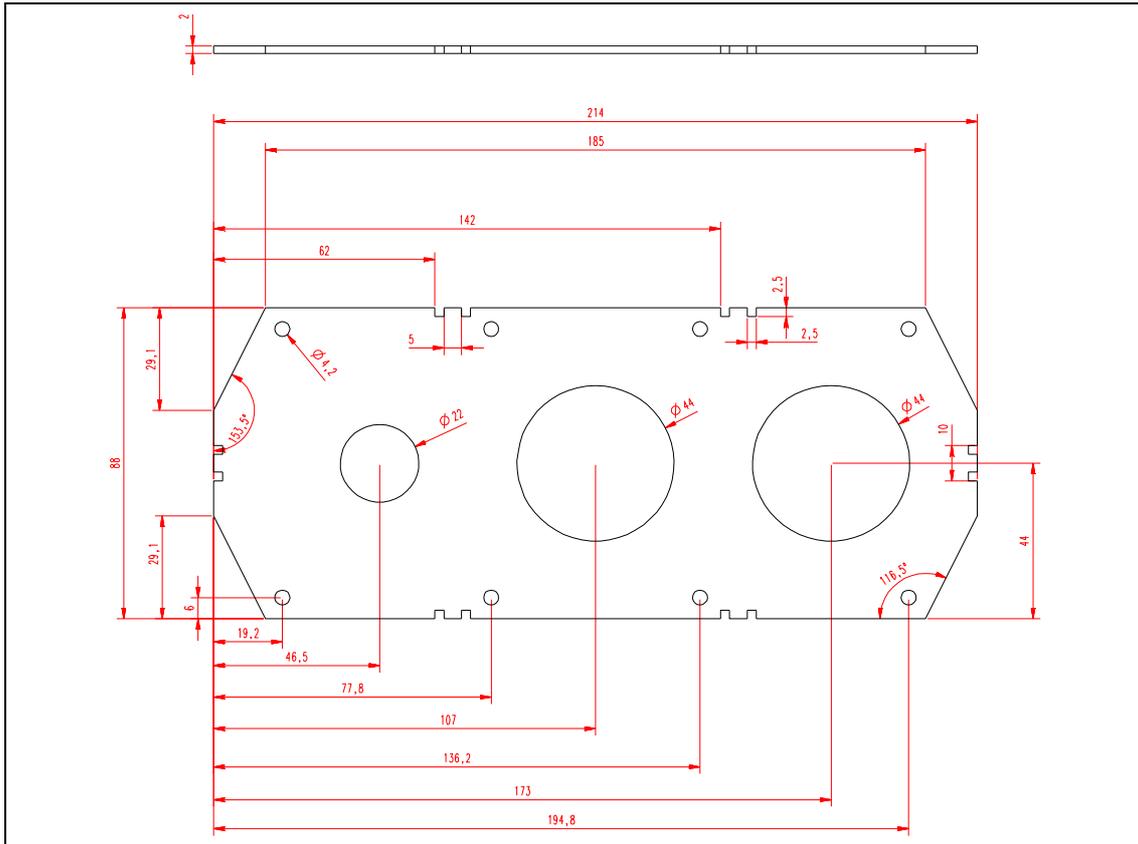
Placa de entrada para cables, MM6, instalación UL.
